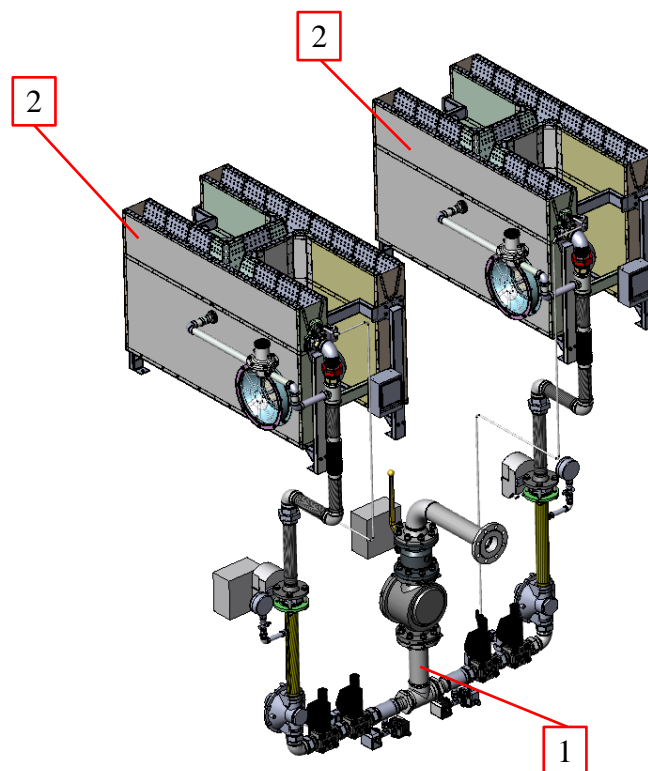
Внешний вид газовой блочной горелки ТЕРМОПОТОК 2x2600НВ
